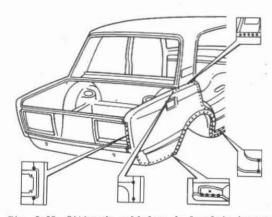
Sitios de soldadura de la aleta trasera. En la vista principal se indican con puntos las costuras de soldadura por contacto. En los fragmentos se indican los sitios de soldadura autógena
